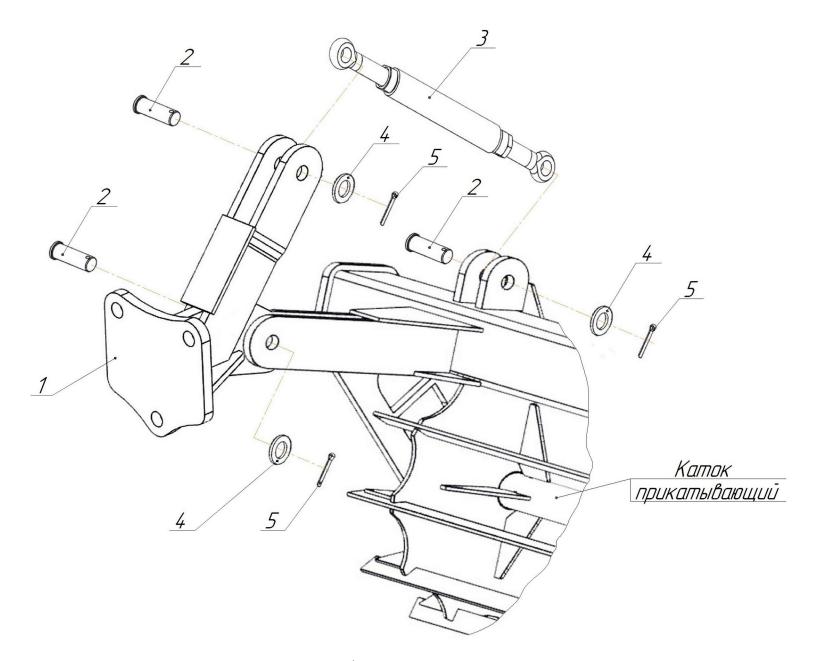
Крепление катка прикатывающего для бороны дисковой прицепной БДП-4000/-02/-03/-04/-05/-06/-08/-09 (PALLADA 4000)
